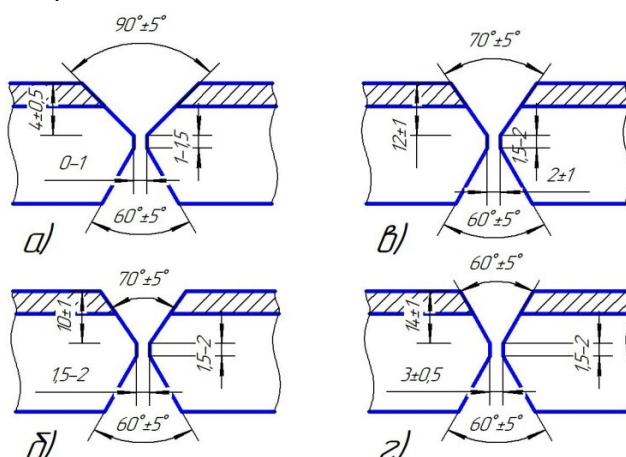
Схема разделки кромок под ручную сварку двухслойных листов с X-образной разделкой кромок: а - для толщин 10-16 мм; б - для толщин 18-22 мм; в - для толщин 24-32 мм; г - для толщин 34-36 мм.
